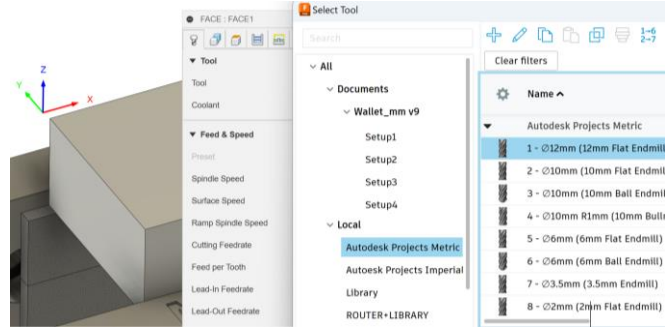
Werkzeug für Planfräsoperation auswählen
